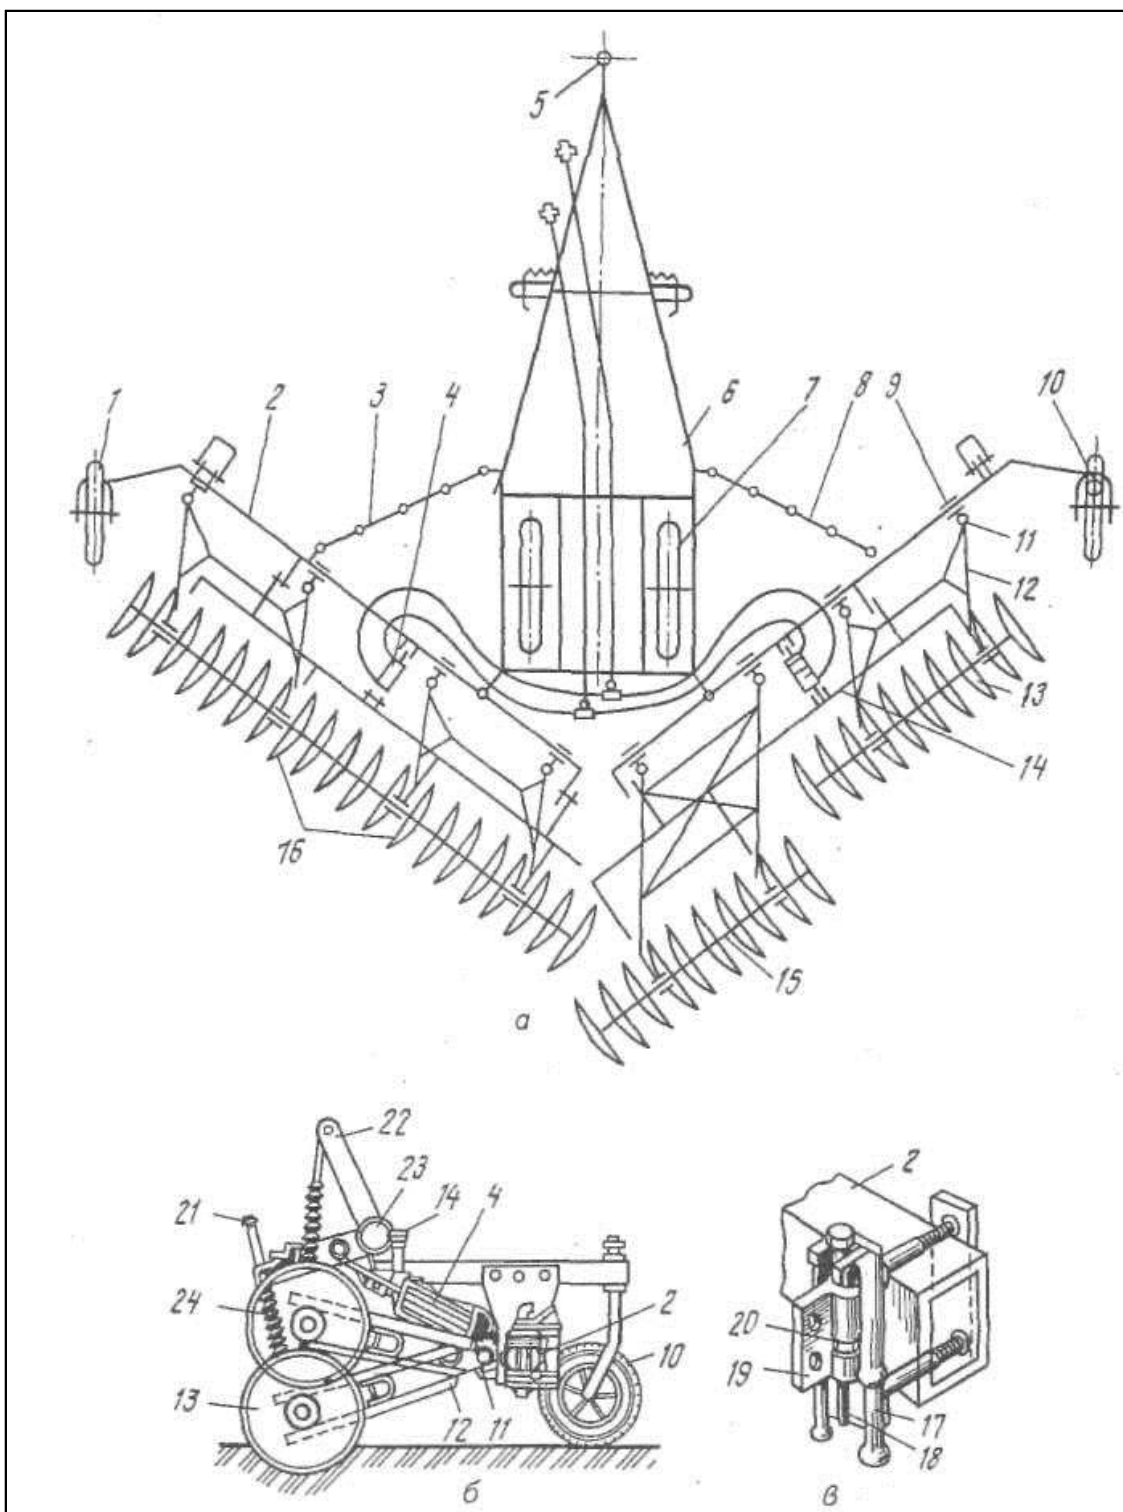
Луцильник ЛДГ-5А: а – общий вид; б – механизм подъема батарей; в – регулируемый понизитель; 1, 7, 10 – колеса; 2 – брус; 3, 8 – тяги; 4 – гидроцилиндр; 5 – серьга; 6 – рама; 9 – хомут; 11 – понизитель; 12 – рамка; 13 – батарея; 14 – труба подъема; 15 – перекрывающая батарея; 16 – диски; 17 – корпус понизителя; 18 – болт; 19 – ползун; 20 – регулировочная гайка; 21 – штанга; 22, 23 – рычаги; 24 – пружина
